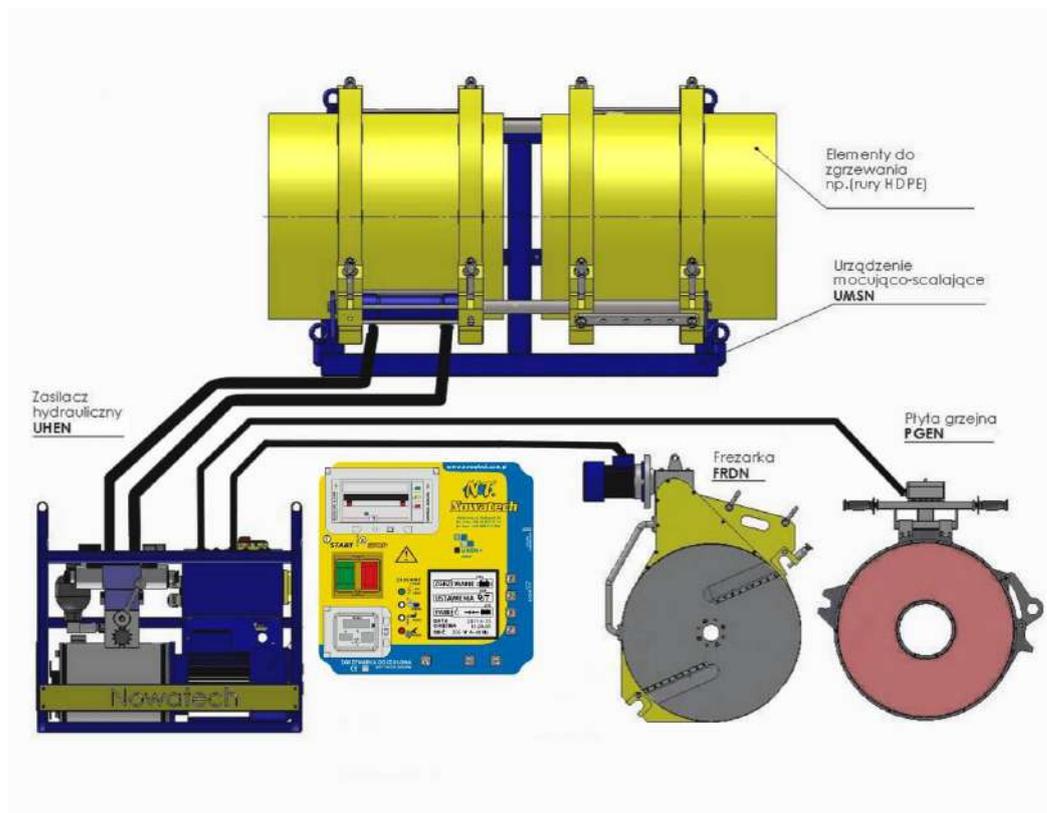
Схема стыкового сварочного аппарата ZHCN-1200E
